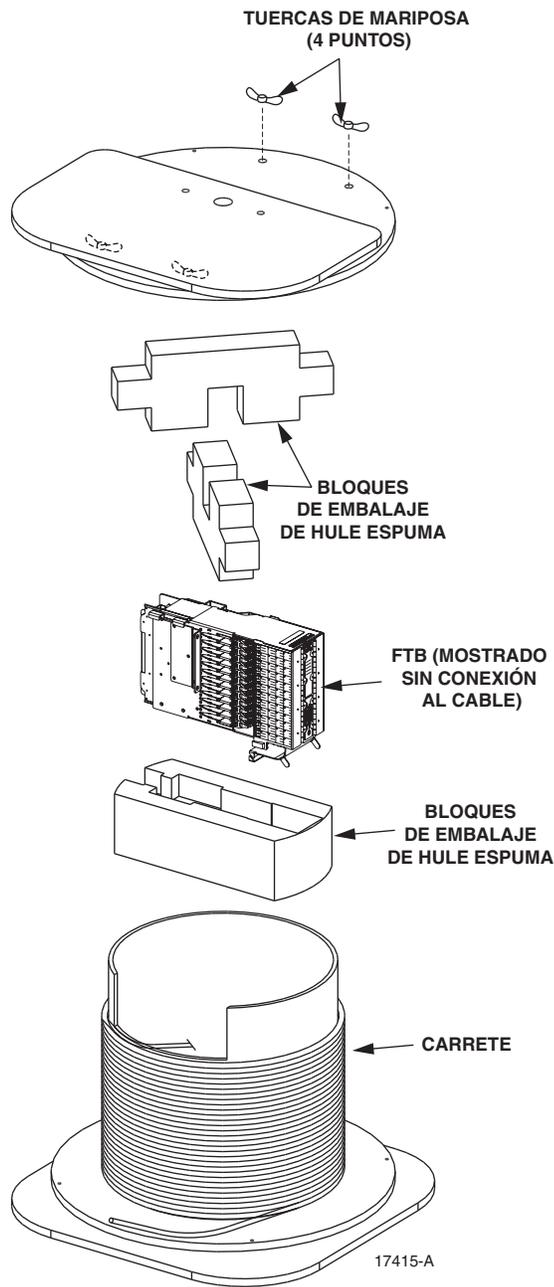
Bloque Preterminado en Fábrica con Cable en Carrete
